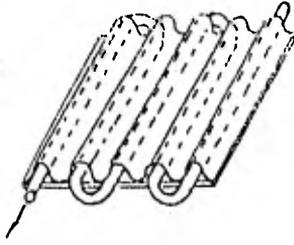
Hierro ondulado soldado a una lámina de metal con tubos de plástico a presión.
